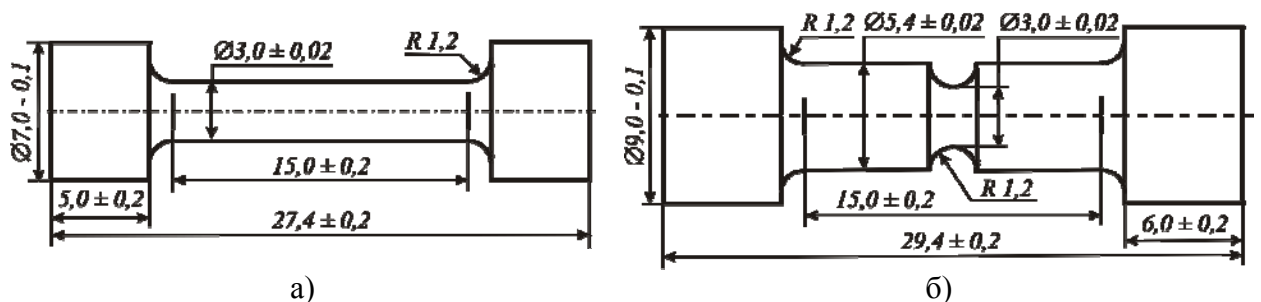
Эскизы цилиндрических образцов на растяжение изборок Э-65 и БМ-7: гладкий образец (а) и образец с концентратором (круговым надрезом) (б)
